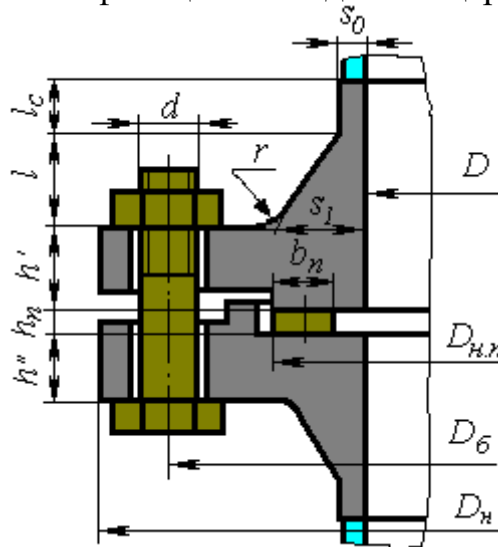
Розрахункова схема верхнього фланцевого з'єднання царги
